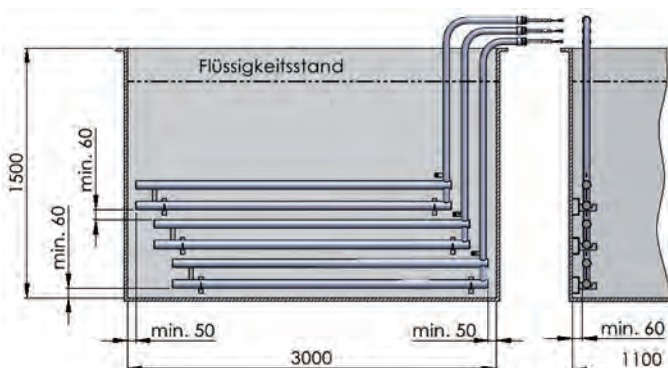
Einbau an der Behälterwand mit Mindestabständen
